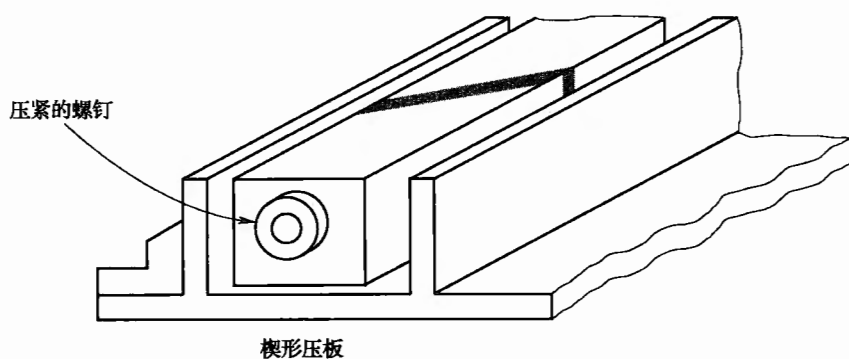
可提高 PCB 刚度和谐振频率的楔形压板
